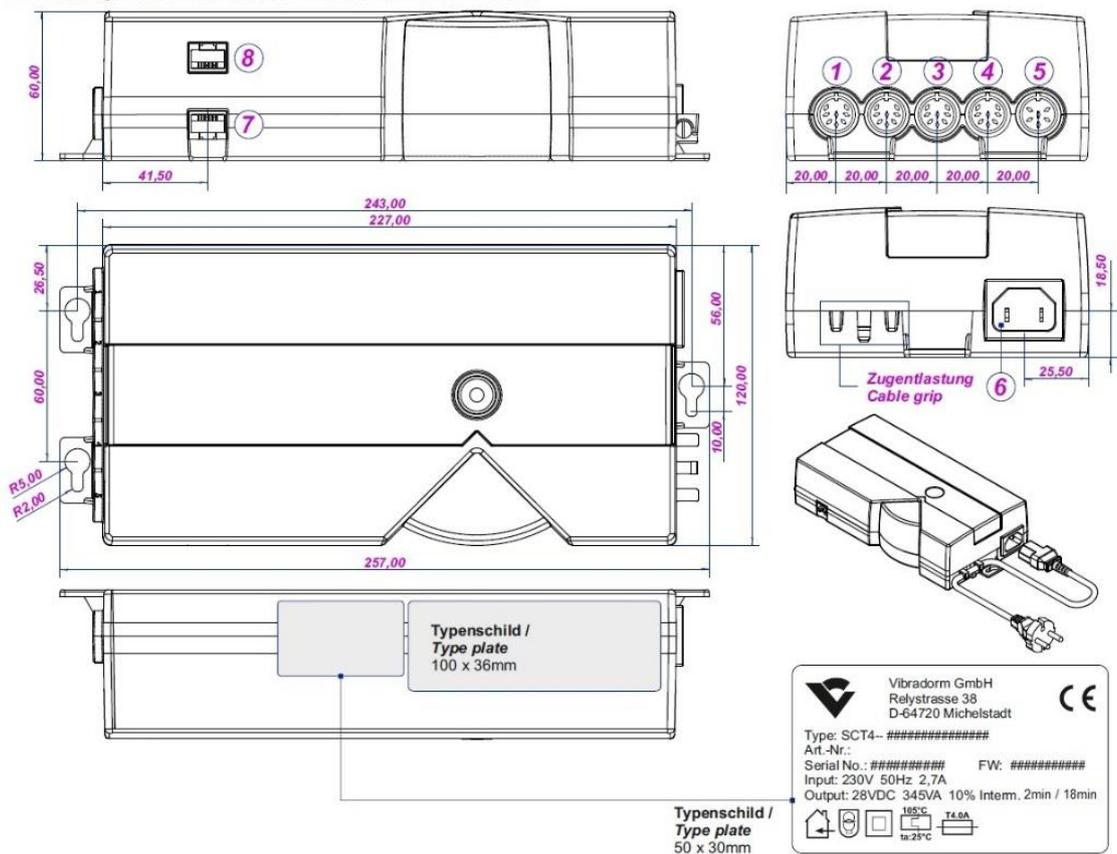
Elektrische Steuerung Abmessungen-Anschlüsse
